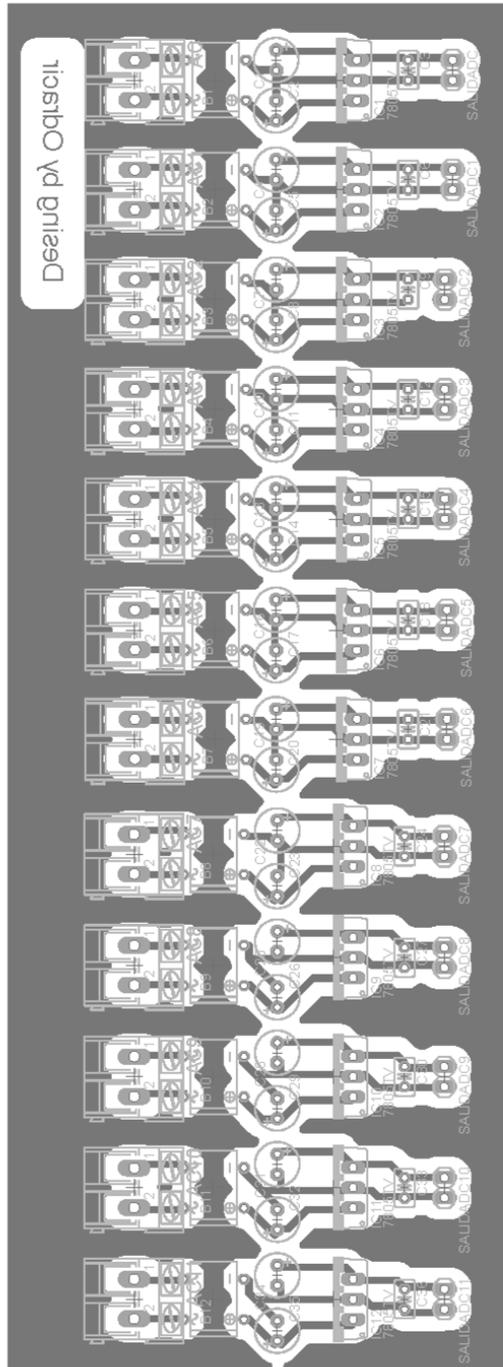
Tarjeta impresa PCB de las fuentes de tensión utilizadas para el acondicionamiento de las señales
